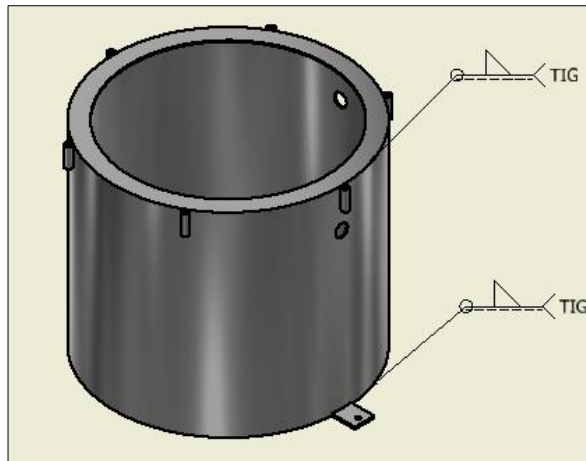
Proceso de soldado para trampa de frío
